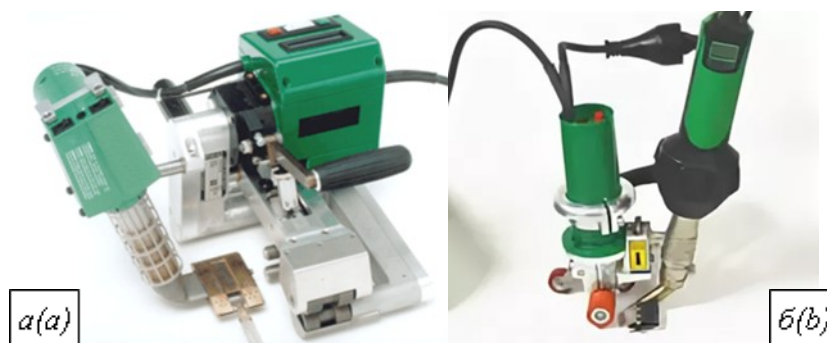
а – одна из моделей сварочного автомата горячего воздуха;
